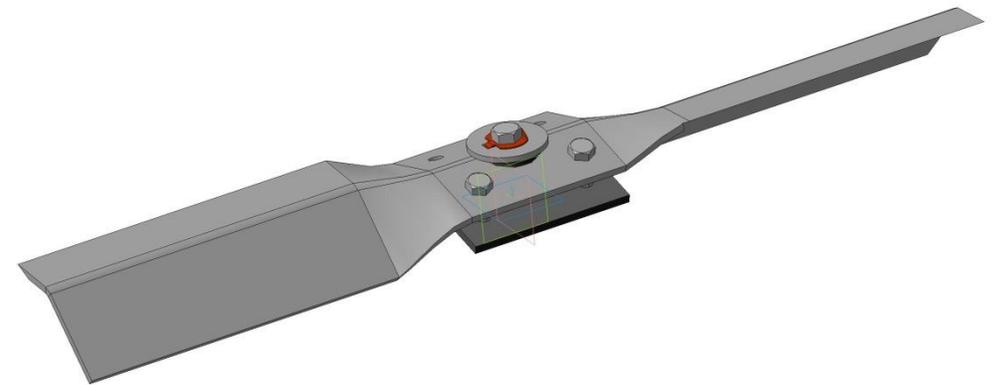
МОЛ 00.490 Нож с креплением в сборе.
